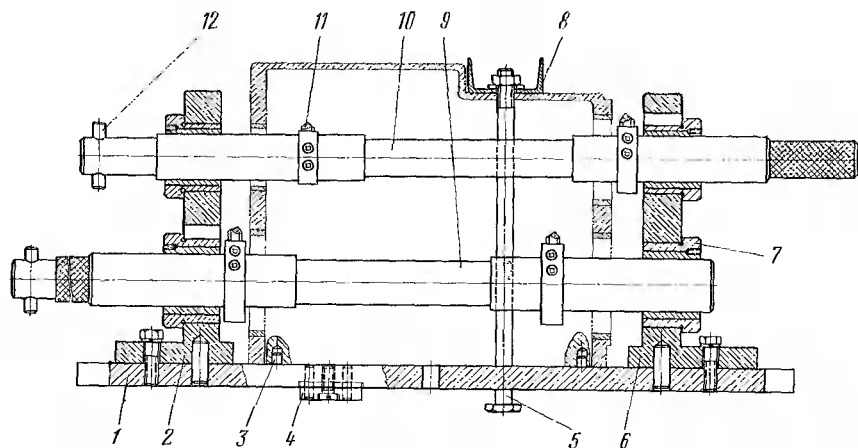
Приспособление для расточки отверстий под подшипники в картере коробки передач:
